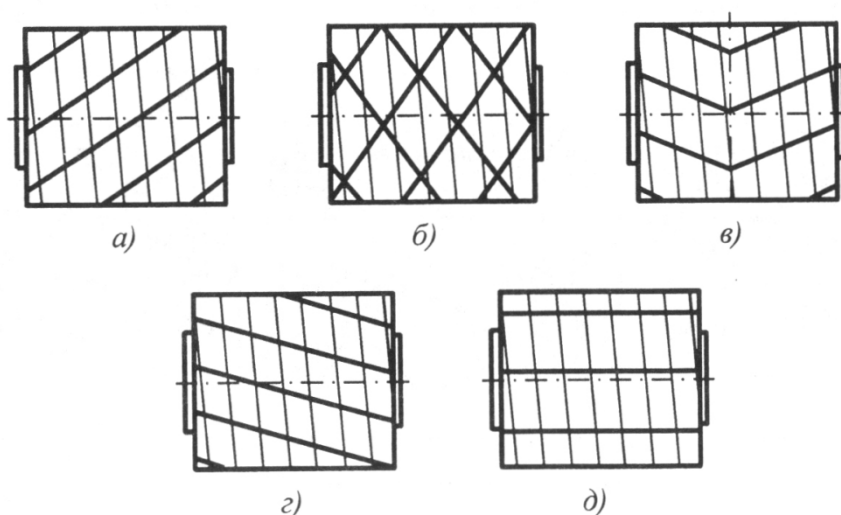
Варианты изготовления стружечных канавок червячных фрез
